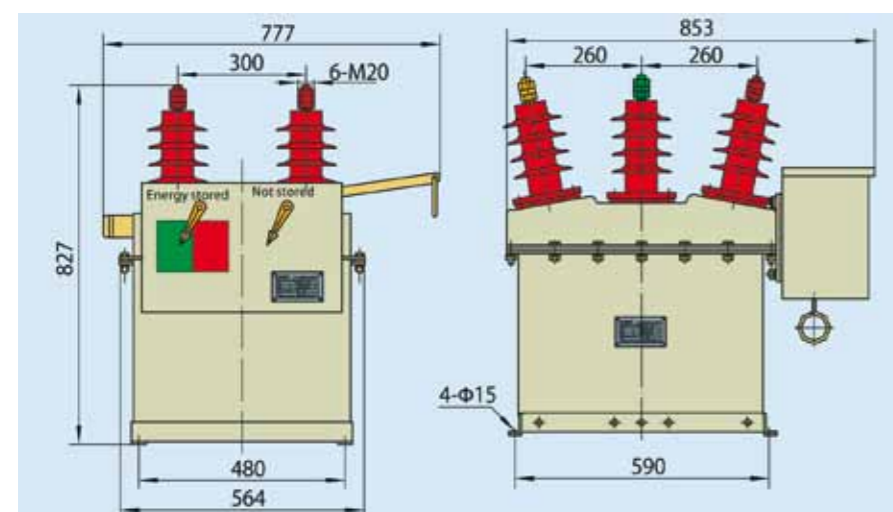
Внешний вид и размеры выключателя ZW8-12
